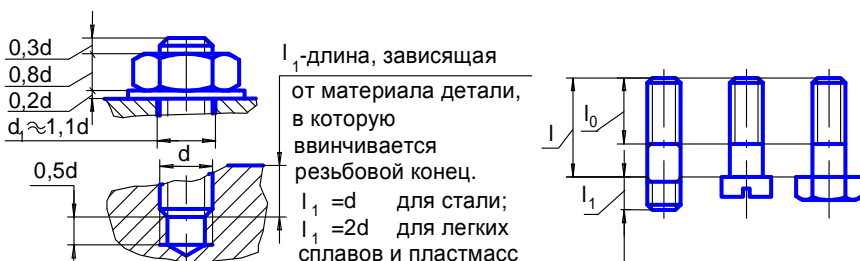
Данные для выбора длины болта, винта и шпильки
